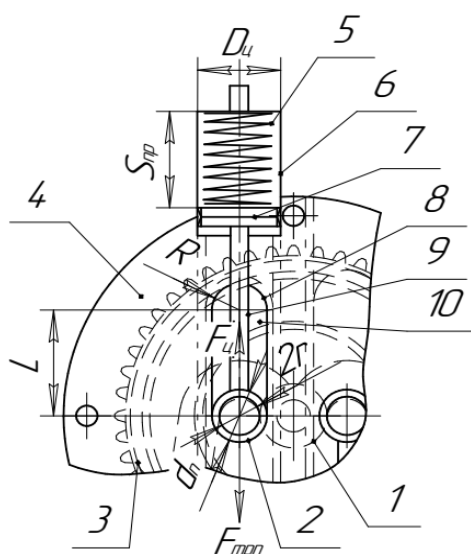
К определению параметров пневмоцилиндра перемещения ползуна: 1 – ступица; 2 – патрубок; 3 – червячное колесо; 4 – крышка пульсатора; 5 – пружина; 6 – пневмоцилиндр; 7 – поршень; 8 – паз; 9 – шток; 10 – ползун
